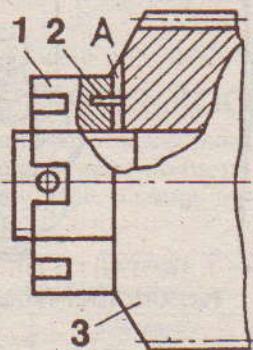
Соединение гайки с шестерней посредством штифта: 1 - гайка; 2 - штифт; 3 - шестерня привода редуктора спидометра; А - паз
